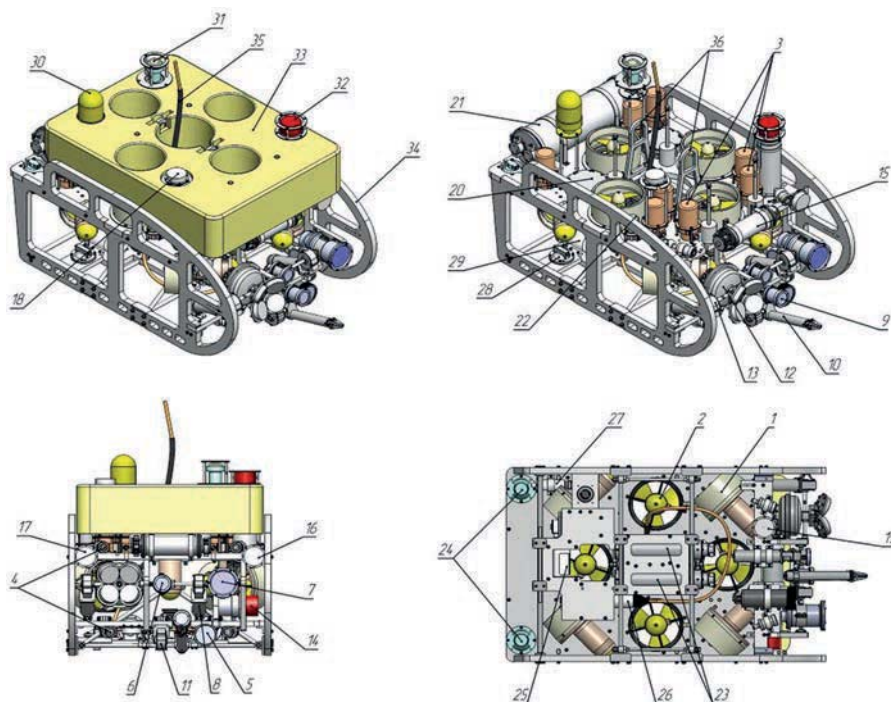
Конструктивный облик ТНПА: 1 – двигатель горизонтальный; 2 – двигатель вертикальный; 3 – БУД; 4 – светильник; 5 – видеокамера; 6 – поворотная цветная видеокамера; 7 – фотокамера; 8 – привод вращения видеосистемы; 10 – захват-манипулятор; 11 – привод поворота захвата-манипулятора; 12 – доплеровский лаг; 13 – привод поворота доплеровского лага; 14 – профилирующий ГСО; 15 – блок электроники ЭЛС; 16, 17, 18, 19 – антенны ЭЛС; 21 – контейнер блока электроники СБУН; 22 – блок управления приводом поворота ДЛ; 23 – блоки энергетики; 24 – компенсаторы давления заборного монтажа; 25 – импульсный светильник; 26 – наконечник кабеля связи; 27 – датчик давления; 28 – компенсатор давления импульсного светильника; 29 – источник питания импульсного светильника; 30 – антенна ГАНС; 31 – приемник СНС со световым маяком; 32 – навигационный ГСО; 33 – блок плавучести; 35 – кабель связи; 36 – рымы крепления грузоподъемного стропа
